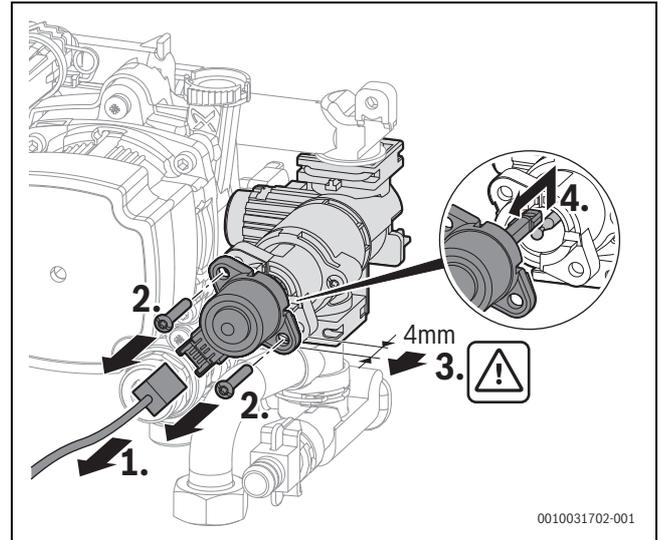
Motor am 3-Wege-Ventil ausbauen (Variante mit Schrauben)
